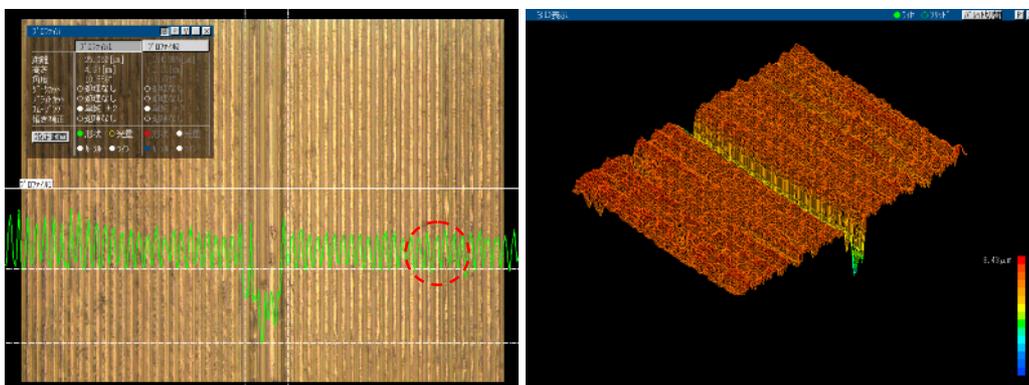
加工形状の観察結果 ( Tool 1 )
